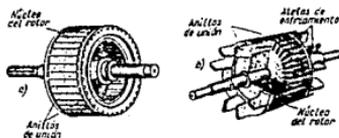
Aspecto exterior y corte parcial de un rotor de jaula de ardilla: a - rotor con devanado en «jaula de ardilla», b - rotor en cortocircuito revestido de aluminio
